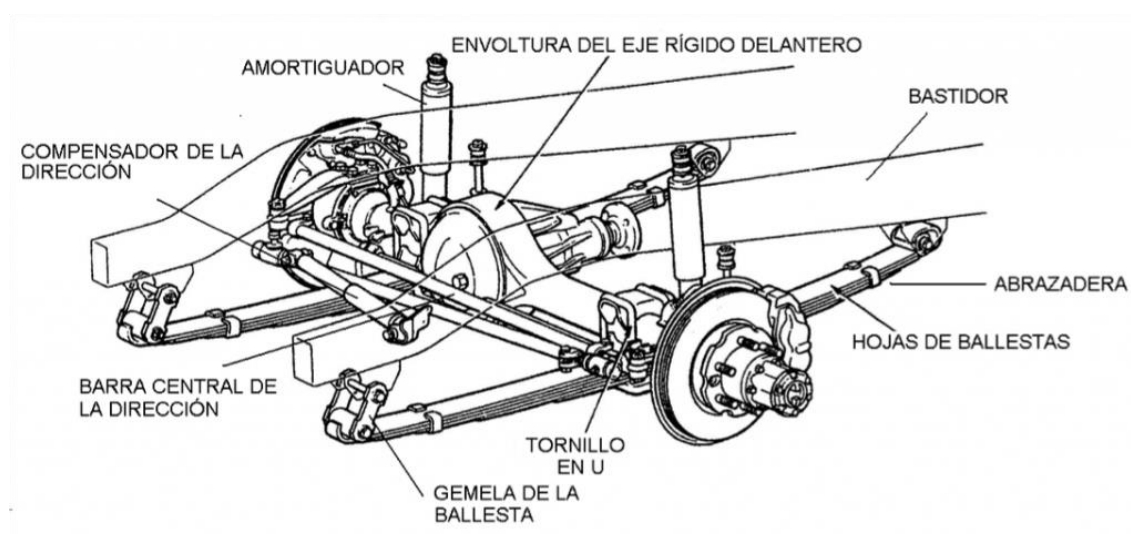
Detalle del eje rígido con ballestas (Fuente: Repuestos TR)
